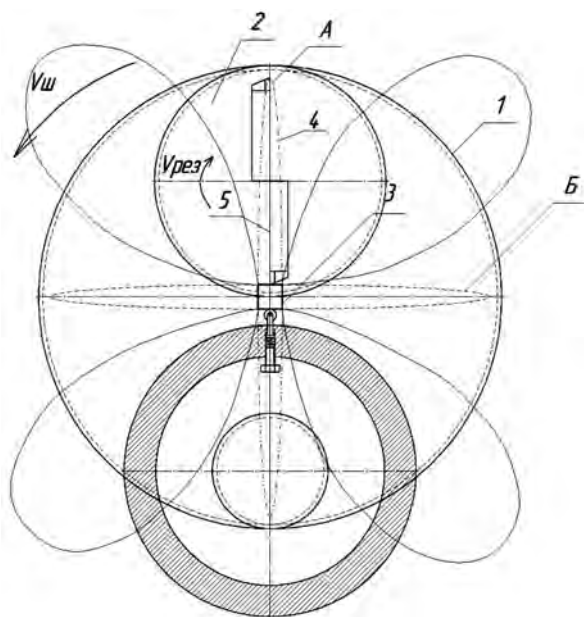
Схемы формообразования гранной поверхности комбинированным движением инструментов
